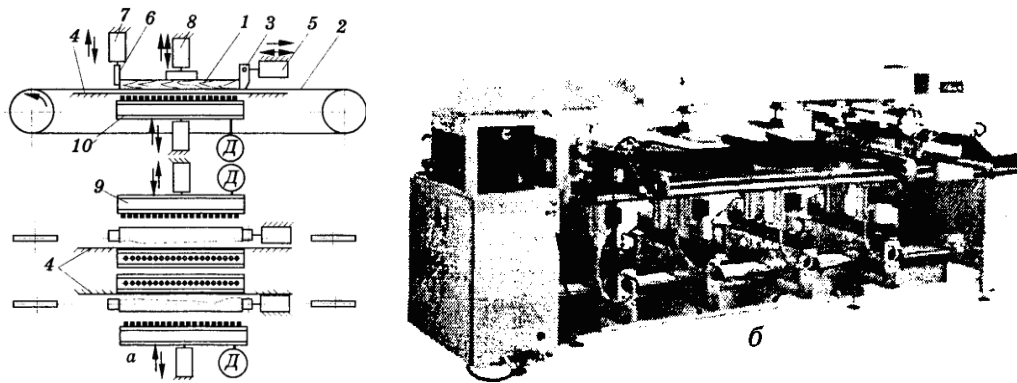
Свердильно-присадний позиційно-прохідний верстат з набором горизонтальних і вертикальних багатошпindelьних головок: а – принципова схема; б – загальний вигляд; 1 – заготівка; 2 – стрічковий конвеєр; 3 – штовхачі; 4 – поздовжні балки; 5, 7 – пневмоциліндри; 6 – упори; 8 – притискачі; 9, 10 – свердильні головки
